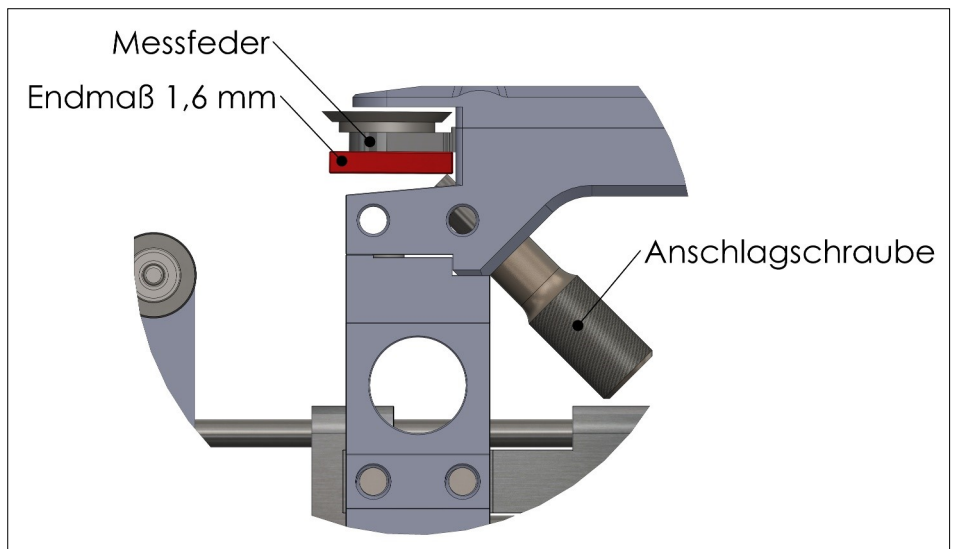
Mini MFA 2 mit Endmaß in Detailansicht
